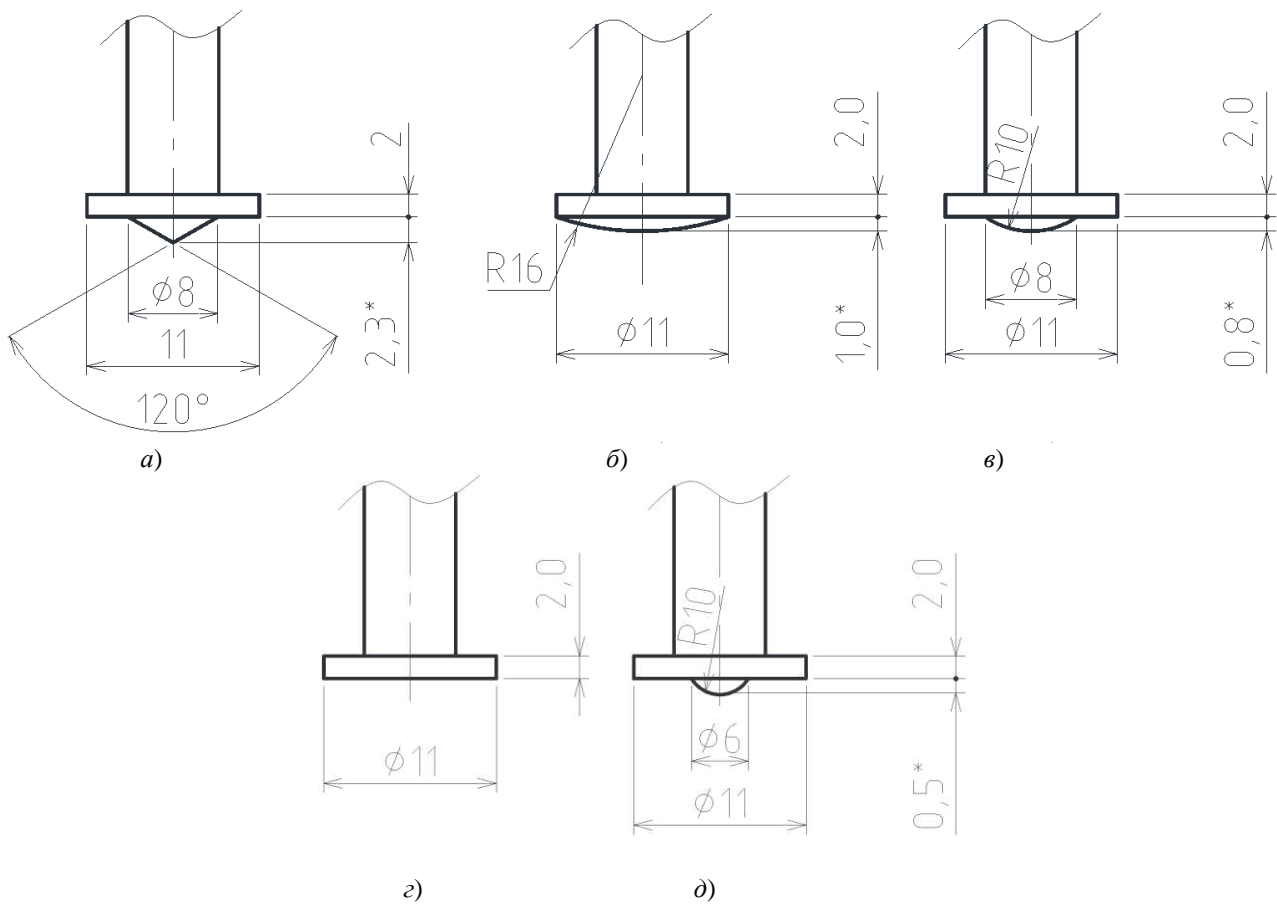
Форма подготовки торцевой части стержня и основные размеры:
